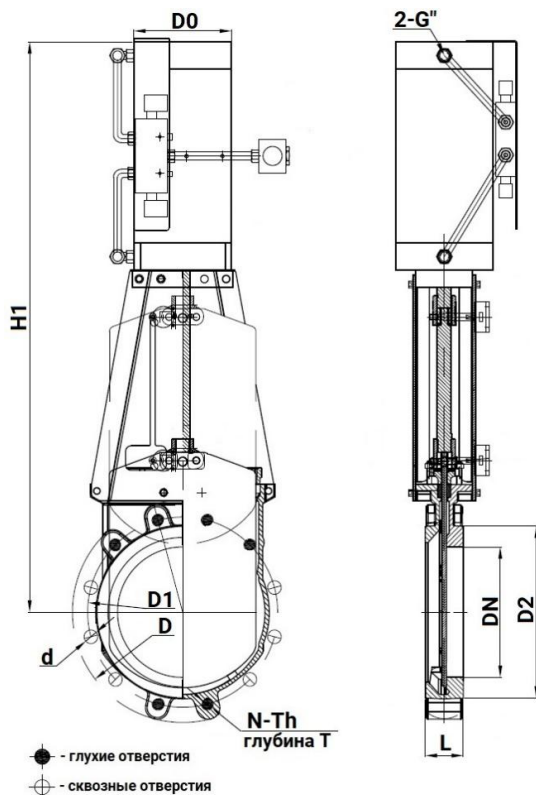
Размеры задвижки в сборе с пневмоцилиндром
